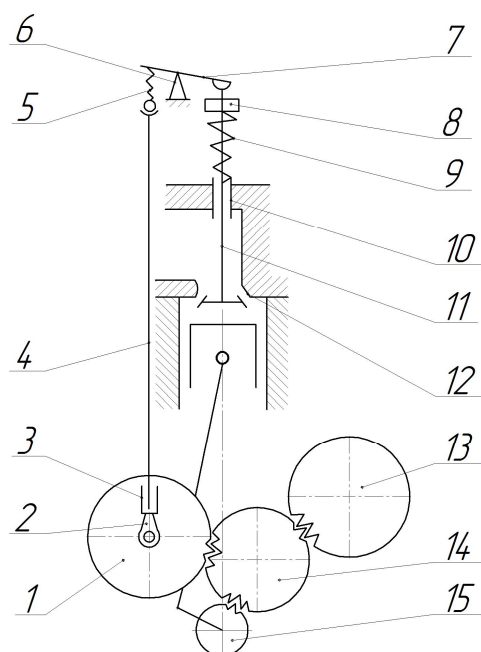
Схема газораспределительного механизма двигателей Д-243, Д-245, Д-260:
